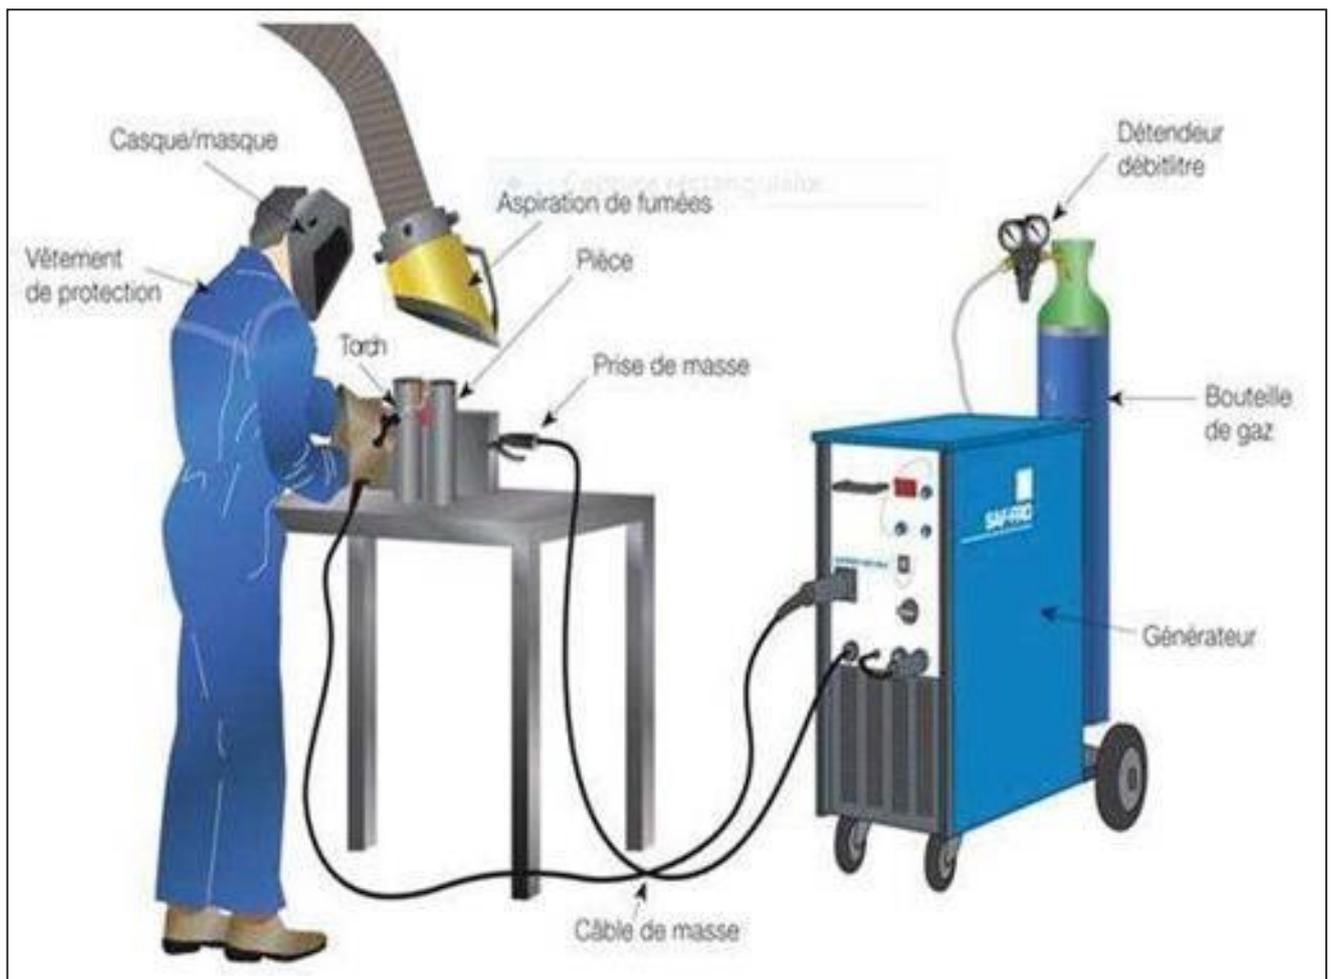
Schéma d'installation manuel pour soudage MIG-MAG [2]
